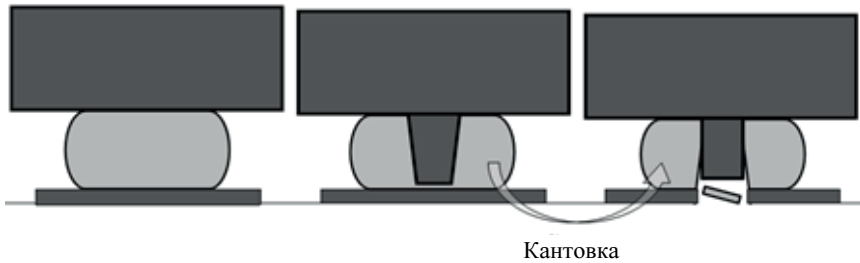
Последовательностьковки заготовки для раскатки [2]
